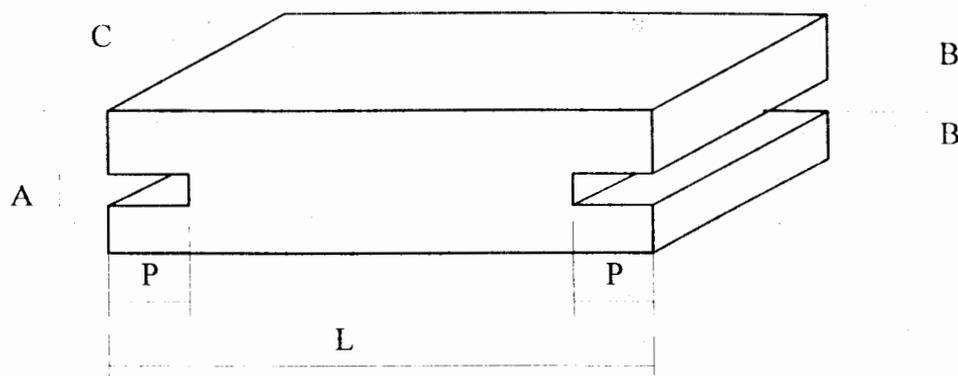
Esboço das peças fabricadas na perfiladeira
